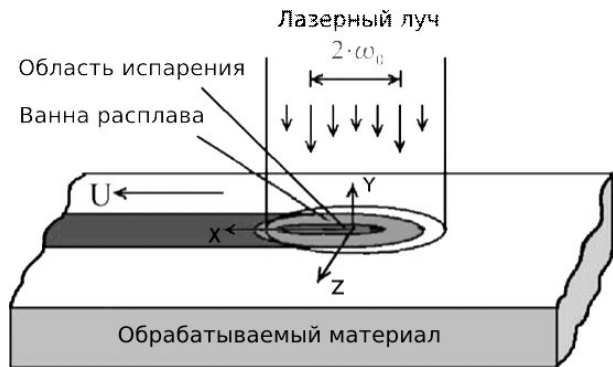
Схема процесса лазерной поверхностной обработки пластины
